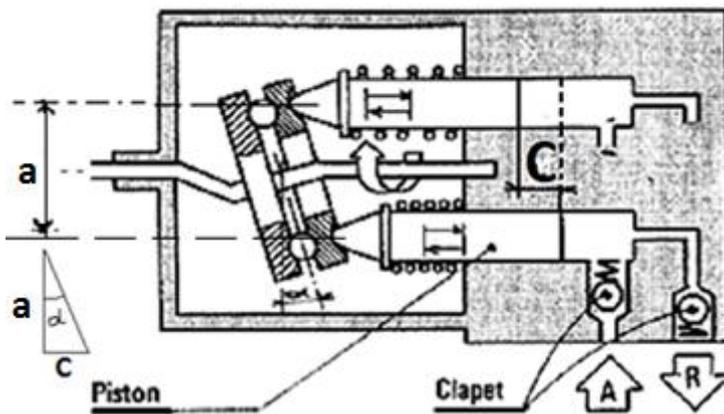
pompe à pistons axiaux à cylindrée fixe
